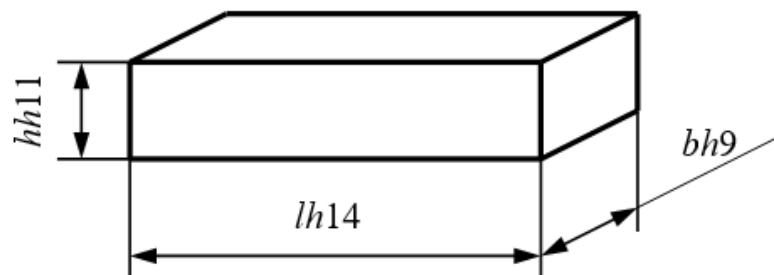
Допуски розмірів призматичної шпонки
